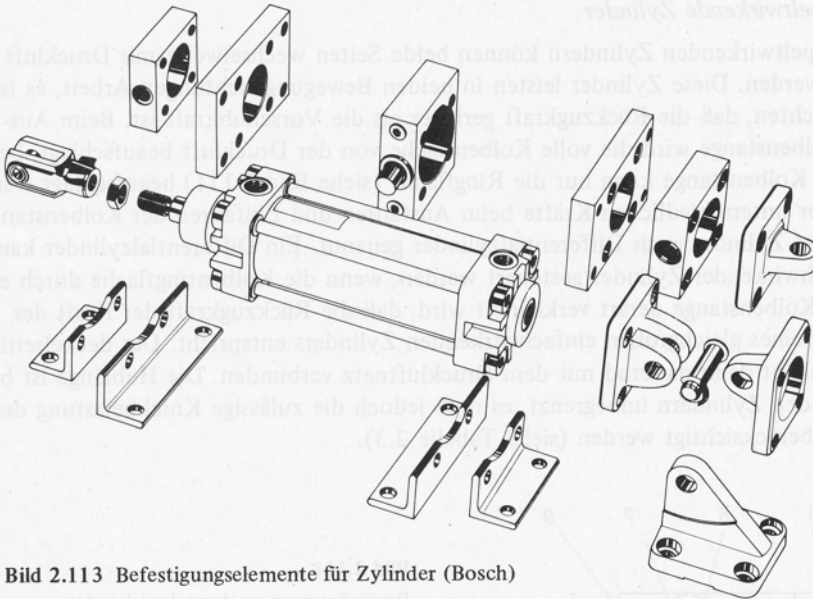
Befestigungselemente für Zylinder (Bosch)
